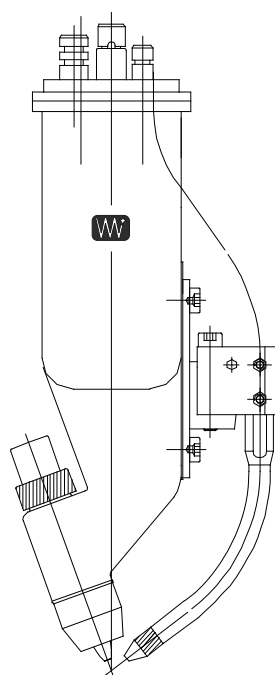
PWM 150 ROB 20° горелка для роботизированной сварки
